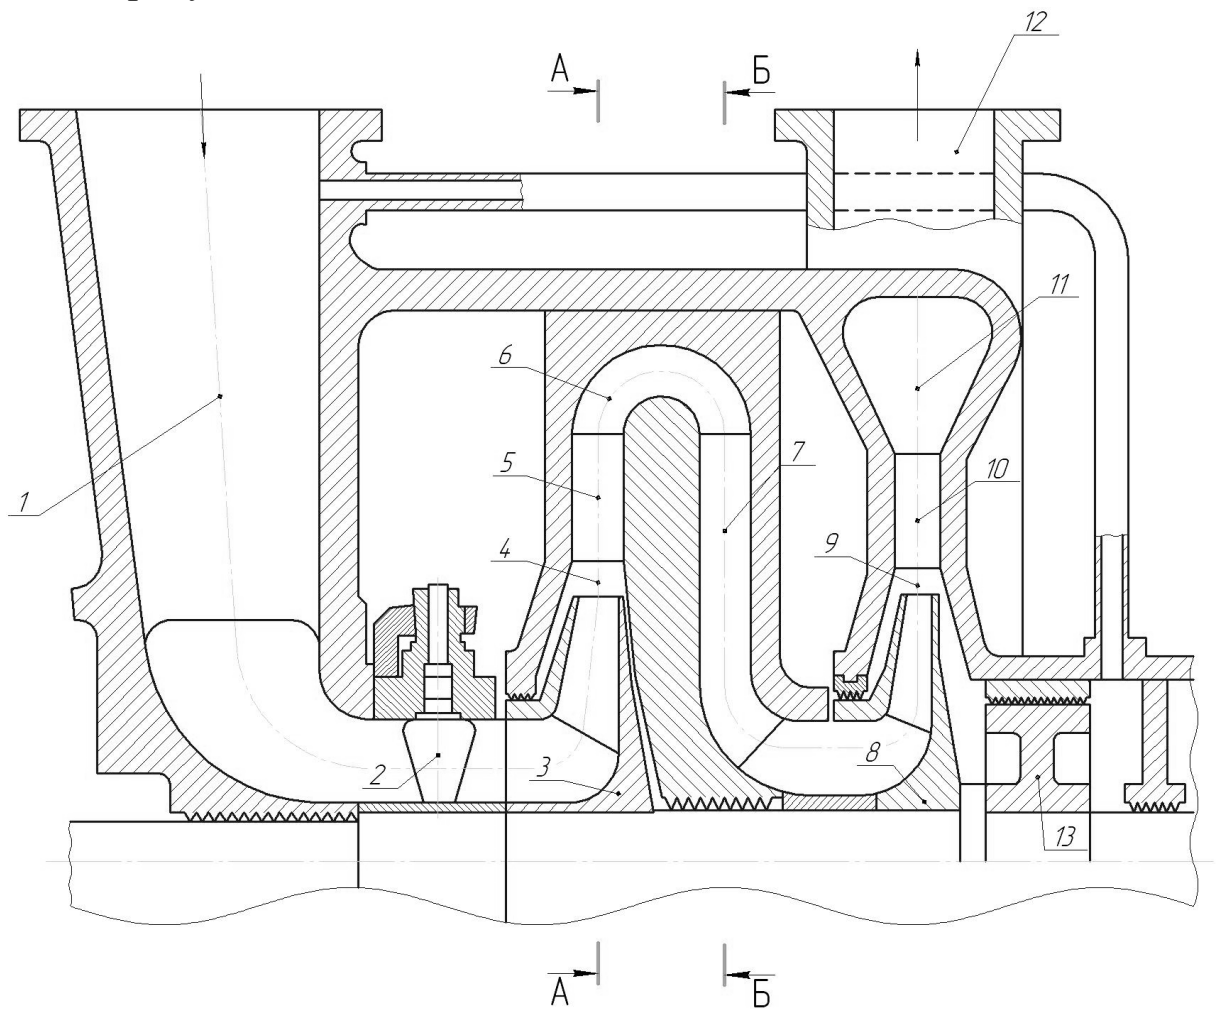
Продольный разрез двухступенчатого центробежного компрессора: 1 – входное устройство; 2 – входной регулирующий аппарат (ВРА); 3 – рабочее колесо первой ступени; 4 – безлопаточный диффузор первой ступени; 5 – лопаточный диффузор первой ступени; 6 – кольцевой поворот (колено); 7 – обратный направляющий аппарат (ОНА); 8, 9, 10 – рабочее колесо и диффузоры второй ступени; 11 – улитка; 12 – выходной патрубок; 13 – думмис (разгрузочный поршень).
